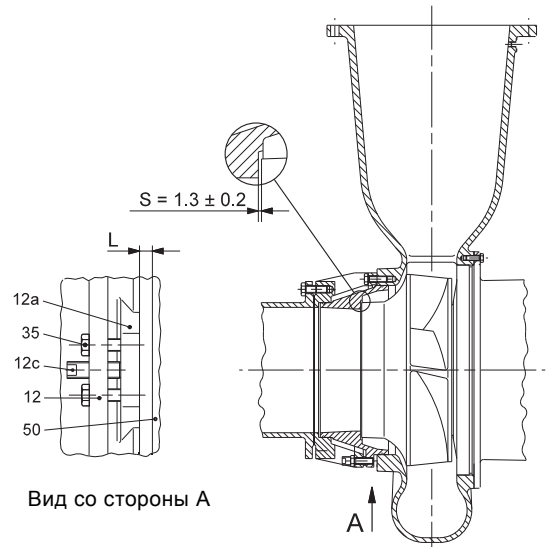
Зазор рабочего колеса, тип установки D и H, метод 2
